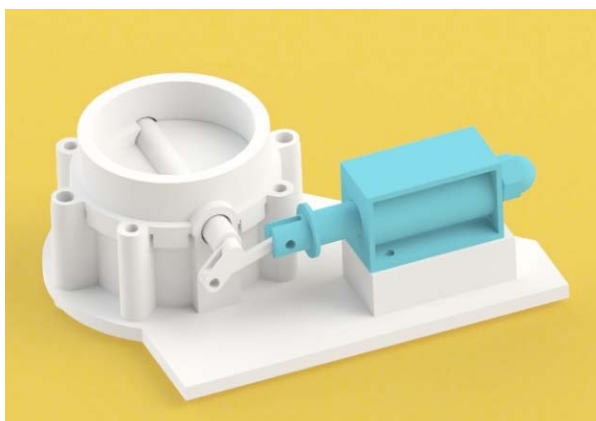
3D модель собственной конструкции вакуумного клапана
